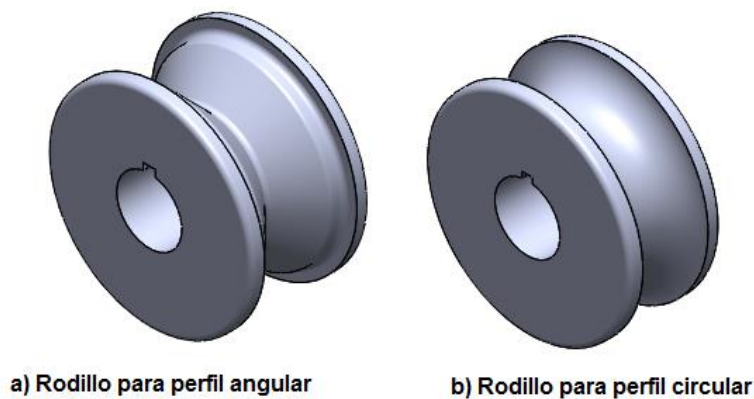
Rodillos de la máquina roladora de perfiles.
